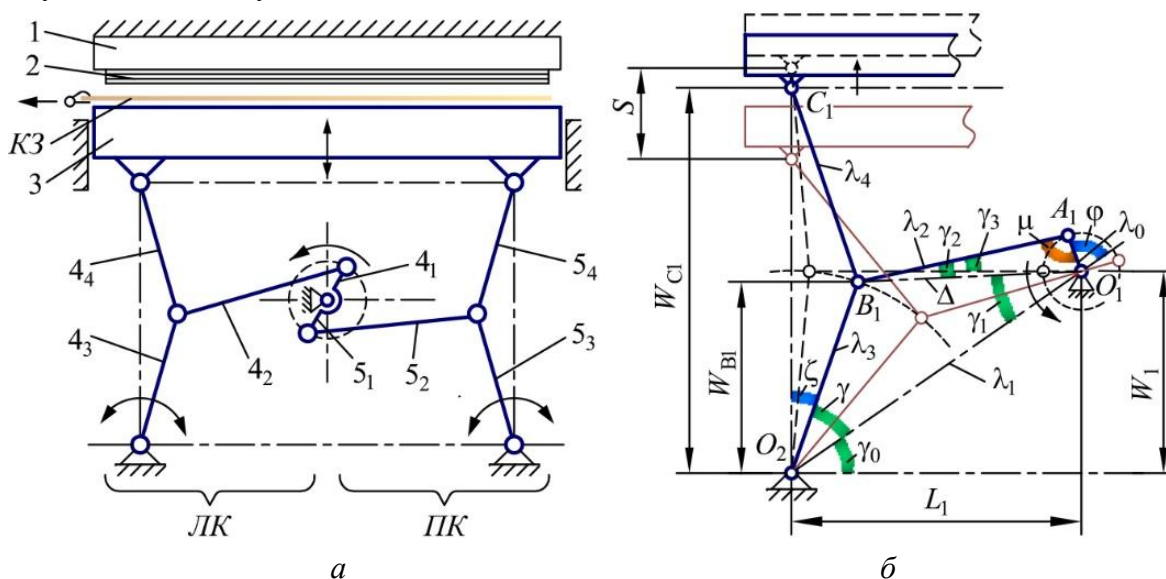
Кінематична схема штанцювального преса (а), схема до розрахунку положень складових розклинювального механізму лівого контуру в приводі натискної плити (б)
